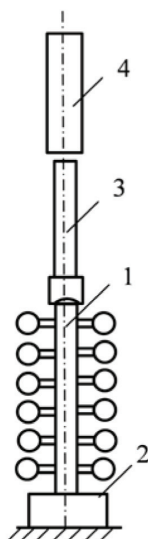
Схема вибро-ударной обработки блока отливок
